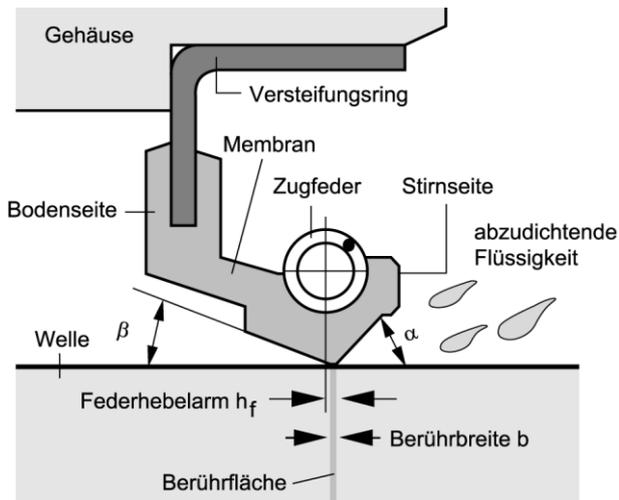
Elastomer-Radialwellendichtring (RWDR) und wichtige Bezeichnungen
